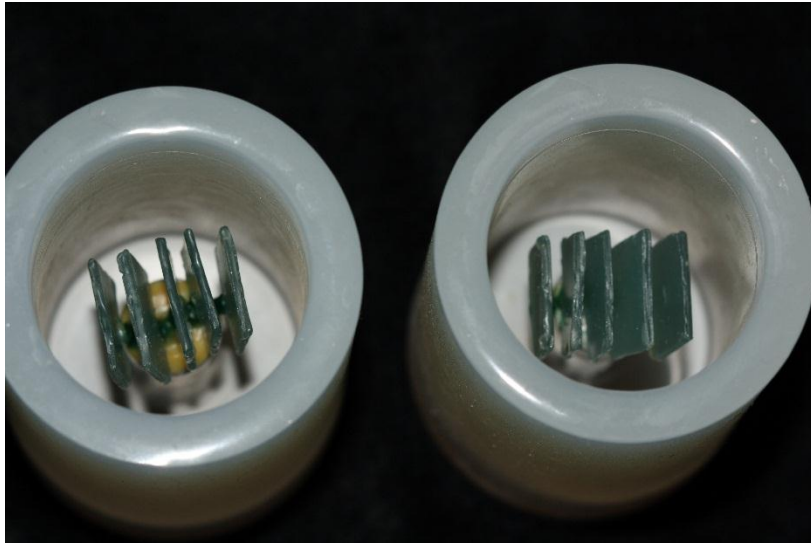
Preparación y montaje de las muestras en el anillo de inyección
